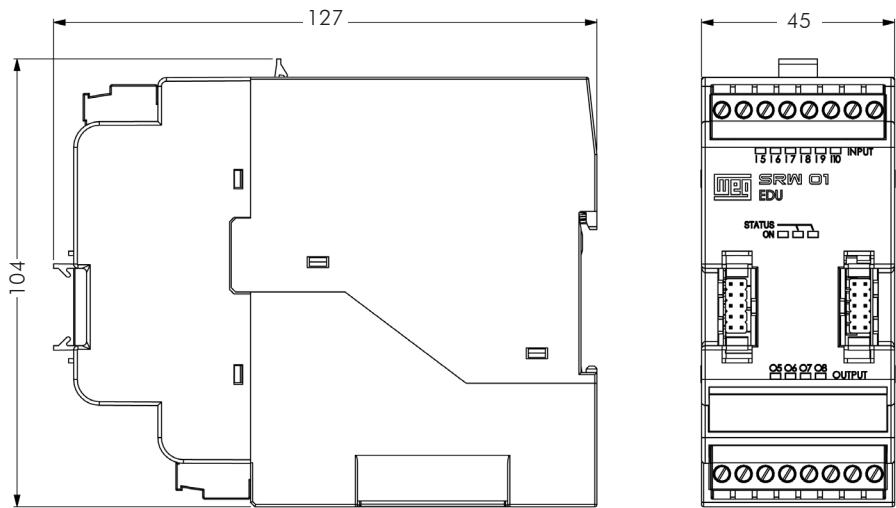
Dimensões da Unidade de Expansão Digital – EDU (mm)
